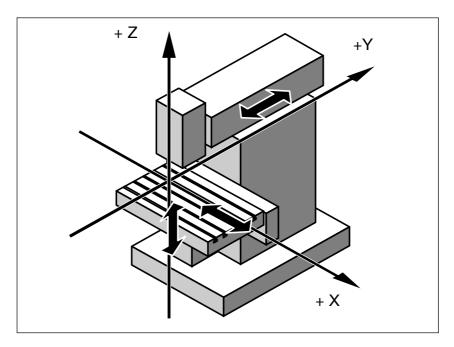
Coordinate/assi della macchina, p. es. di una fresatrice
